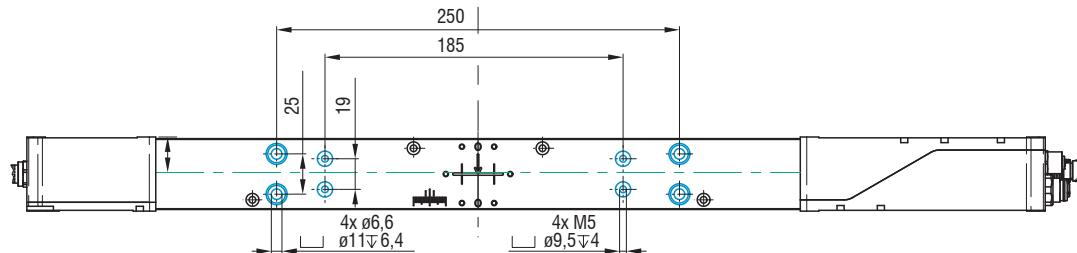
Maßzeichnung Montageschiene ODC2700-40(002), optionale Montage
